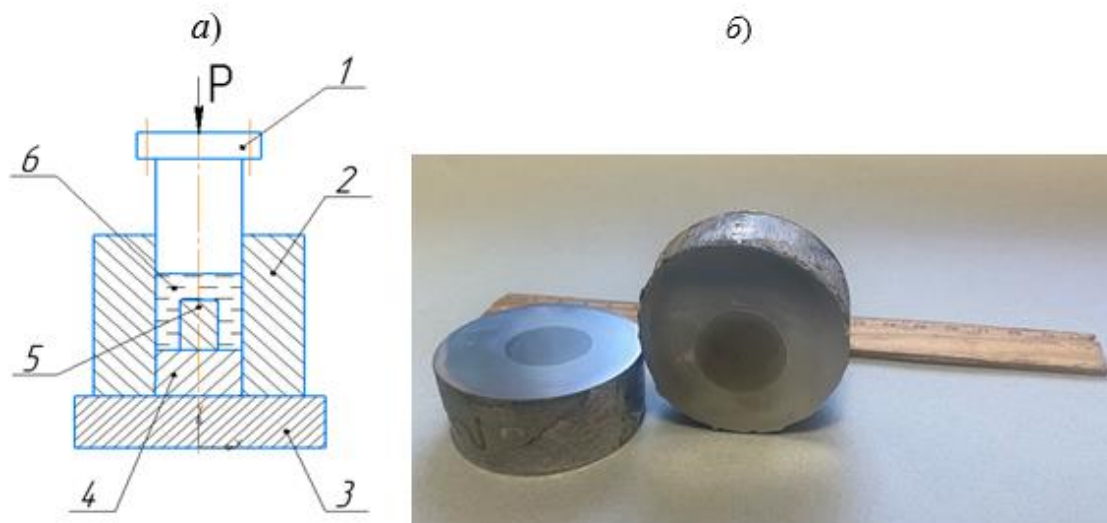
a* – принципиальная схема литья с кристаллизацией под давлением жидкого металла и спеченного рабочего вкладыша 1 – верхний пуансон, 2 – матрица, 3 – плита пресса, 4 – нижний пуансон, 5 – рабочий вкладыш, 6 – жидкий металл
